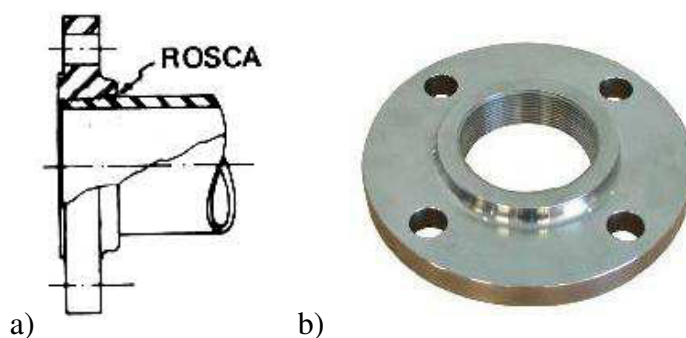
a) Desenho Representativo de um Flange Rosqueado (SENAI, 1997). b) Flange Rosqueado (AHAD Tubeline co., 2012)
